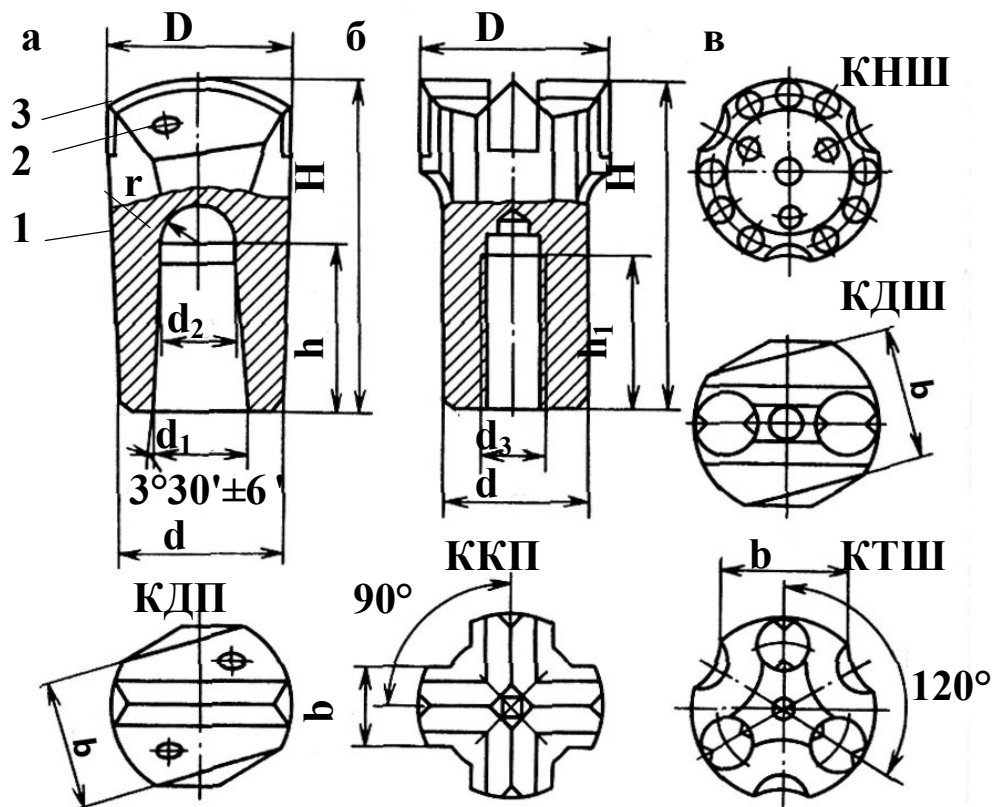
Буровые коронки: а – с конусным отверстием; б – с резьбовым отверстием; в – вид с торца типов КДП; ККП; КНШ; КДШ; КТШ (размеры, мм:  $D$  – диаметр головки,  $d$  – диаметр корпуса,  $d_3$  – диаметр резьбы,  $H$  – высота коронки,  $h_1$  – длина резьбы,  $b$  – толщина лезвия)
